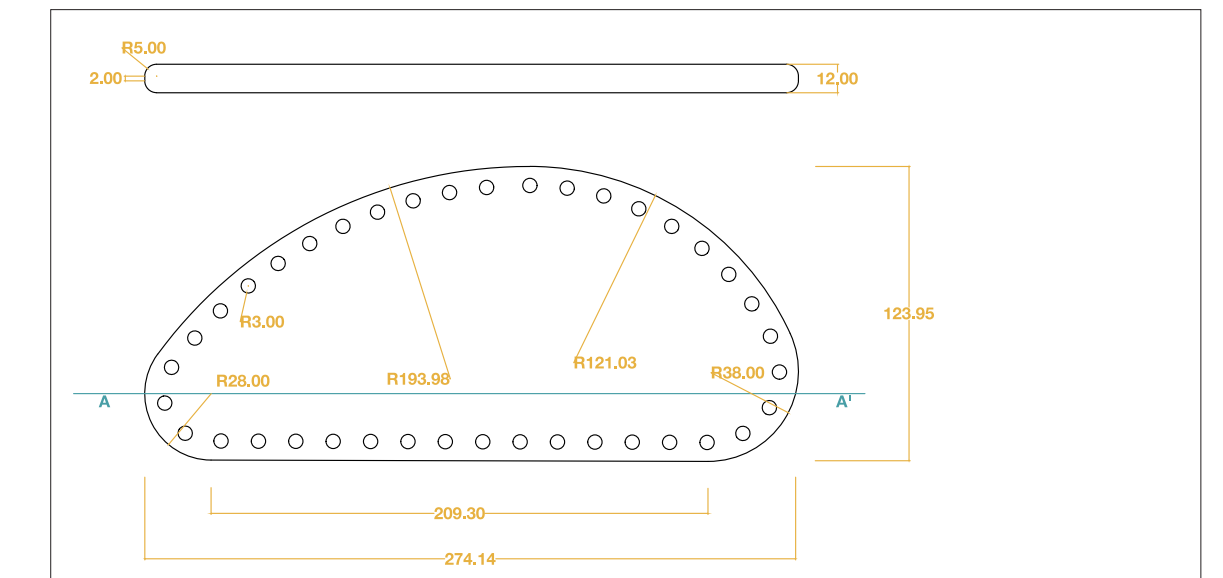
Planta y alzado de la *Cubierta 213*.
